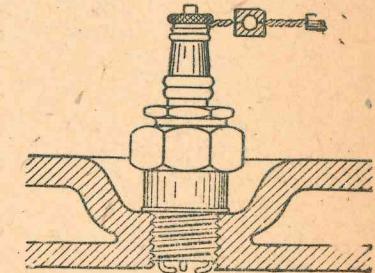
Расположение свечи на газогенераторной головке и устройство искрового зазора.
